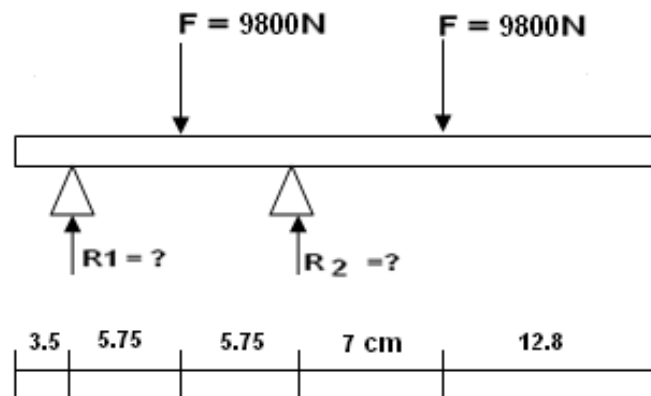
DIAGRAMA DE FUERZAS QUE ACTUAN EN LOS RODAMIENTOS
